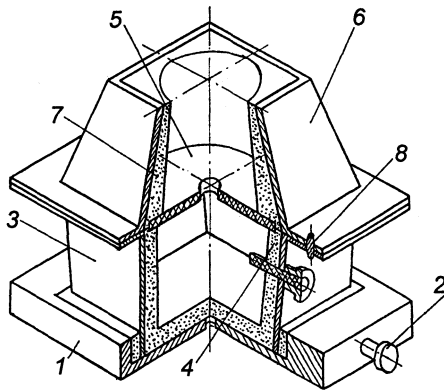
Металлооболочковая литейная форма: 1 – поддон литейной формы; 2 – транспортировочные цапфы; 3 – нижняя полуформа; 4 – облицовочный огнеупорный слой; 5 – стержень-перемычка; 6 – верхняя полуформа; 7 – облицовочный огнеупорный слой; 8 – центровочные элементы
